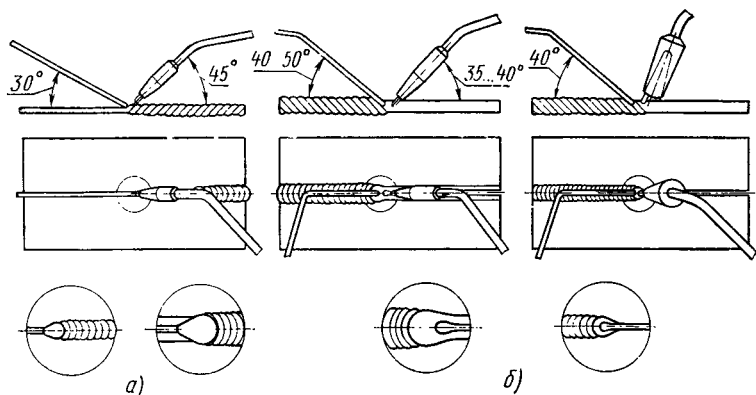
Способы газовой сварки (в нижнем положении):
